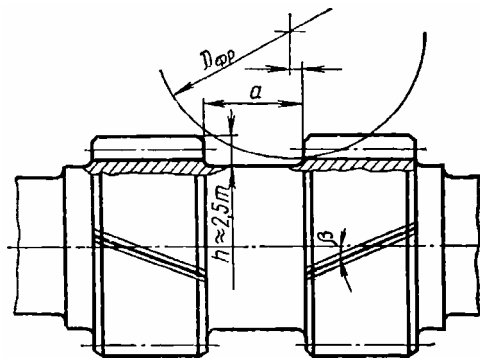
Конструкция вала – шестерни шевронной зубчатой передачи
